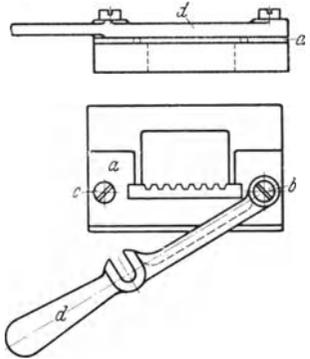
Einspannvorrichtung für einseitig zu bearbeitende Werkstücke. *a* Querführung; *b* Drehpunkt; *c* Anschlagstift; *d* Spannhebel mit Handgriff.
